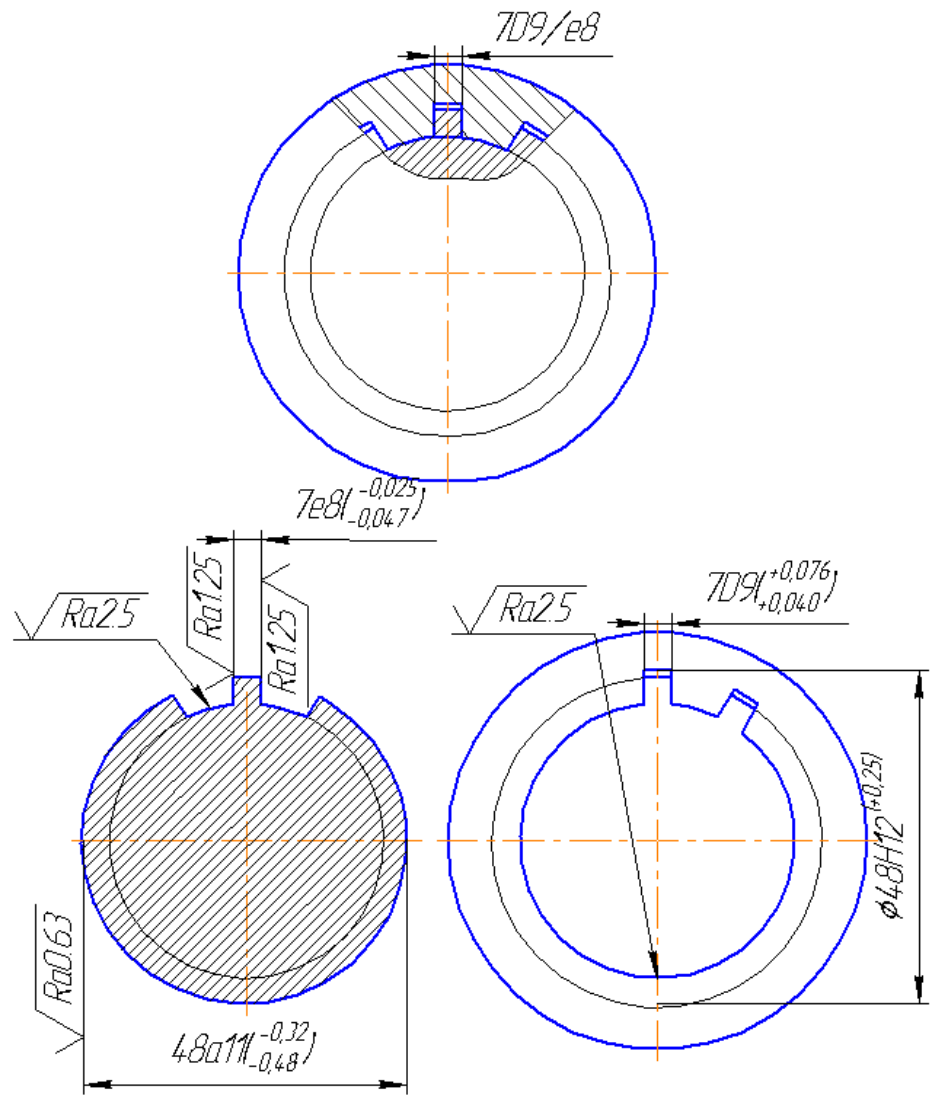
Сборочный и подетальный эскизы шлицевого прямобочного соединения
